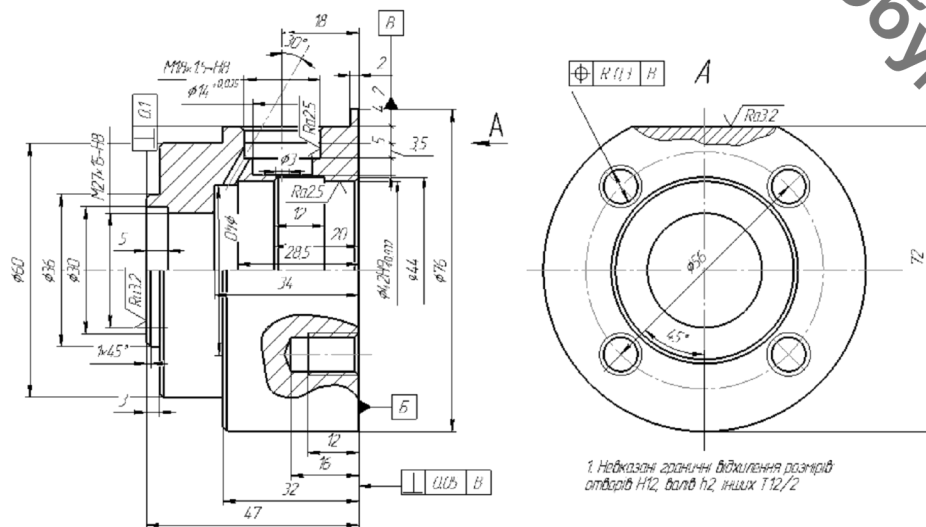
Ескіз деталі «Корпус клапана Г.36.004»
